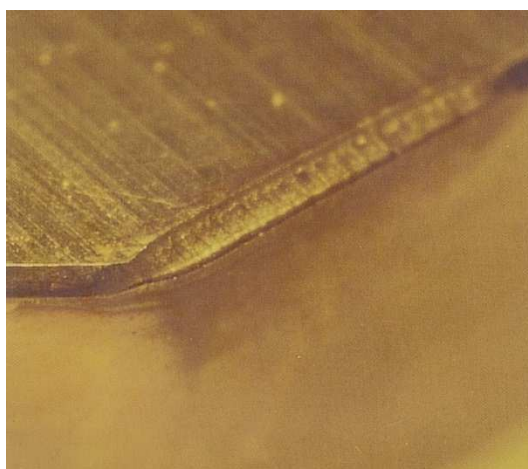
Desgaste por fissura térmica na ferramenta (Silva, 2008)
